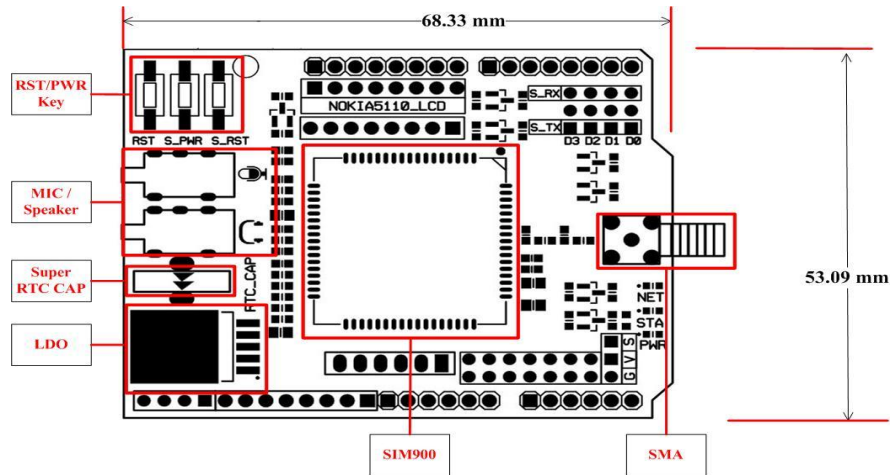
Dimensiones mecánicas de ECom GPRS/GSM Shield
